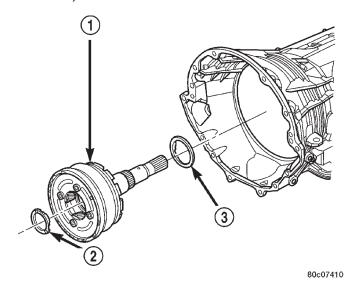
Desmontaje del juego de engranajes planetarios de impulsión y marcha atrás
